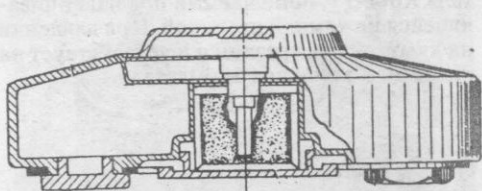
Чертеж противотанковой мины РТ Мi-Ва
